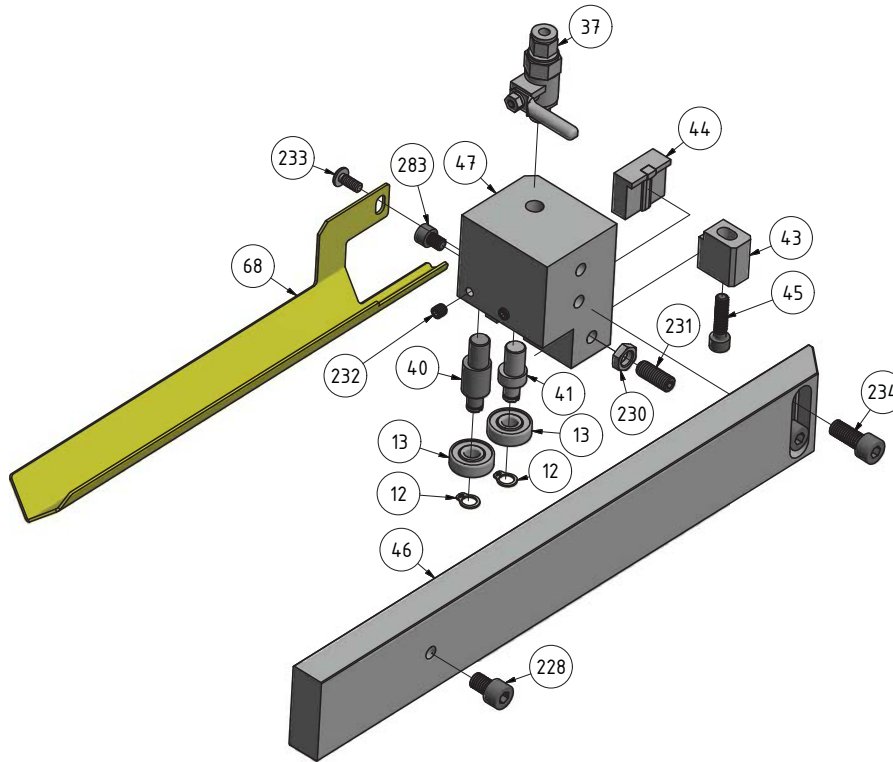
Explosionszeichnung - Drawing spare parts
